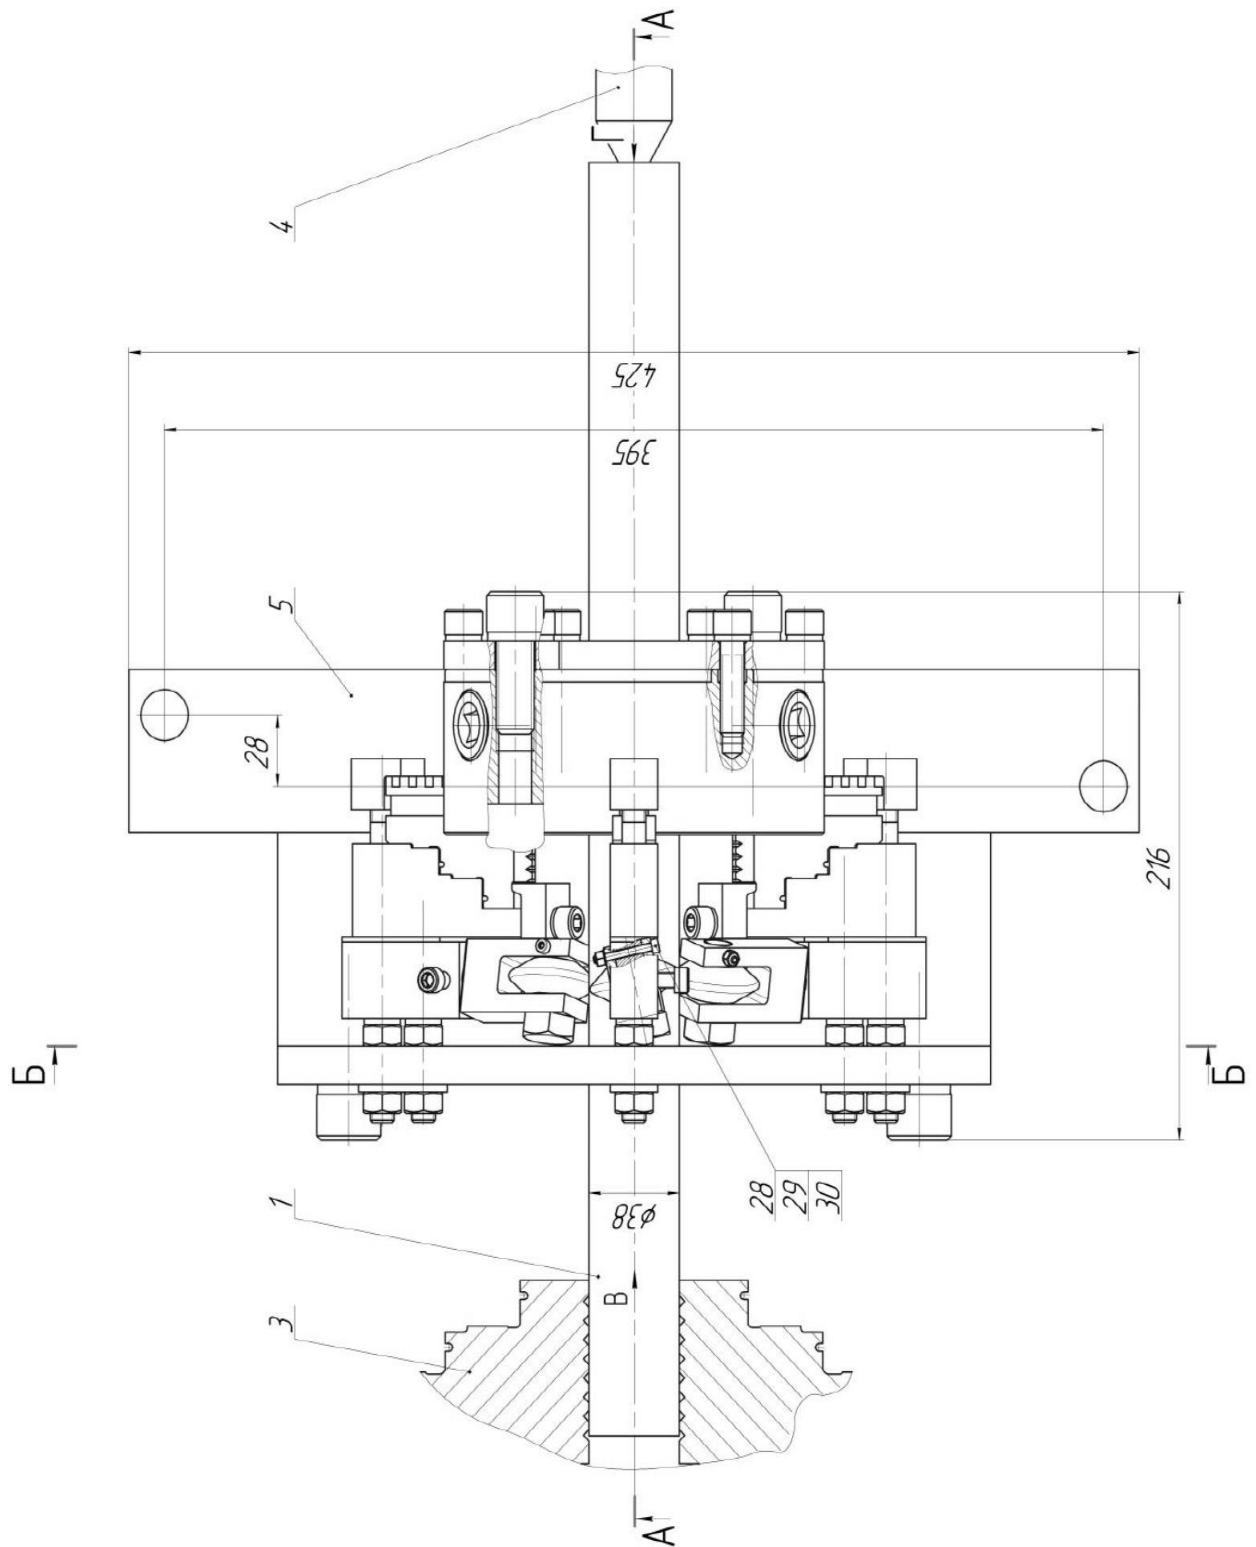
Трироликова обкатна головка (вид зверху)
